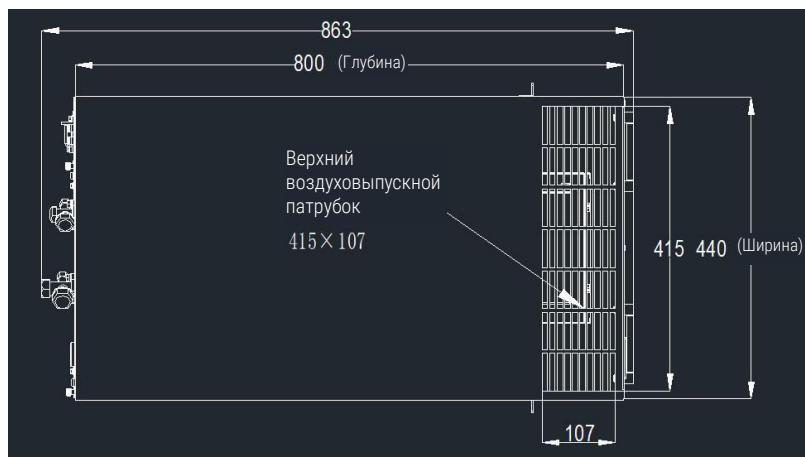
Чертеж габаритных размеров внутреннего блока мощностью 7,5 кВт
